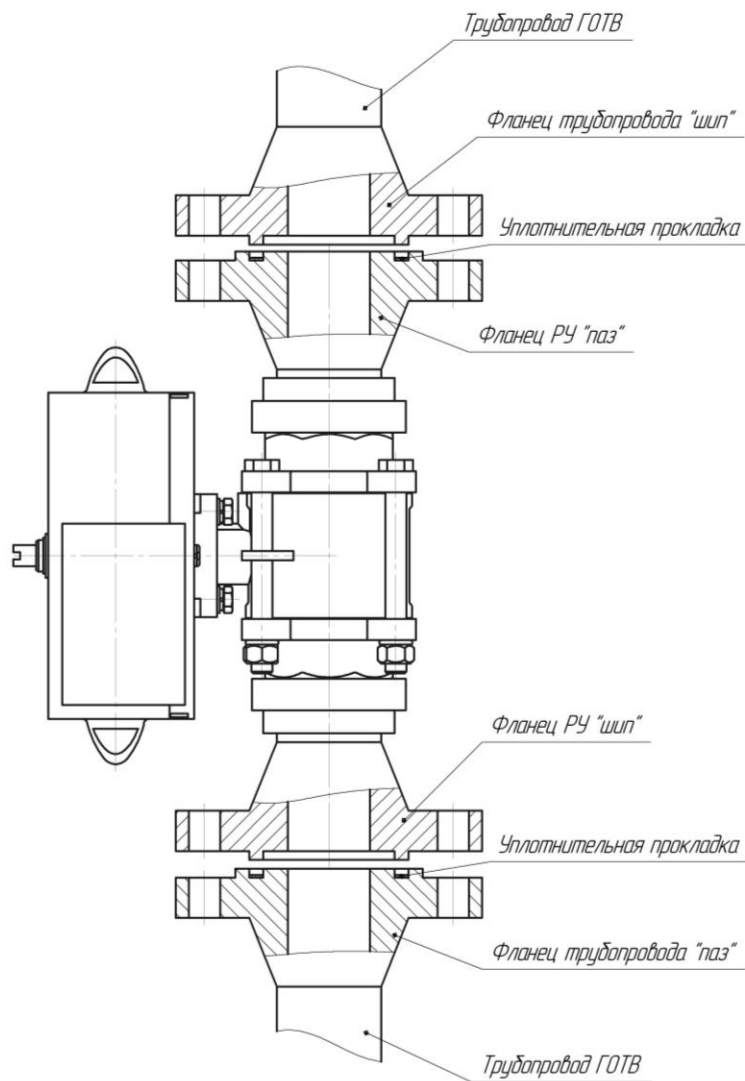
Схема монтажа устройства распределительного на трубопроводе
